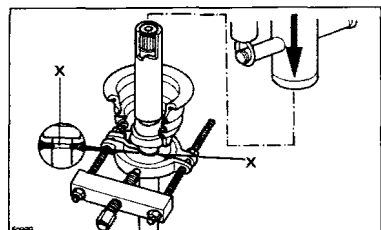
Напрессовка гофрированного чехла вала привода левого колеса вместе с подшипником с применением оправки Т.Ав.944
